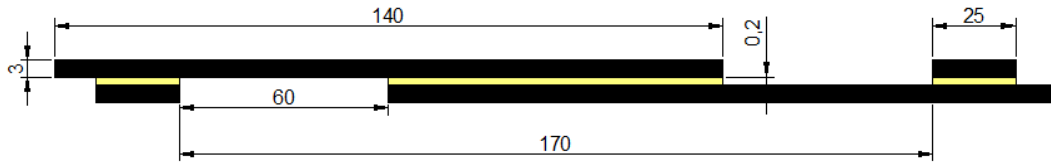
Geometria e dimensões das juntas de L_0 de 50 mm.
